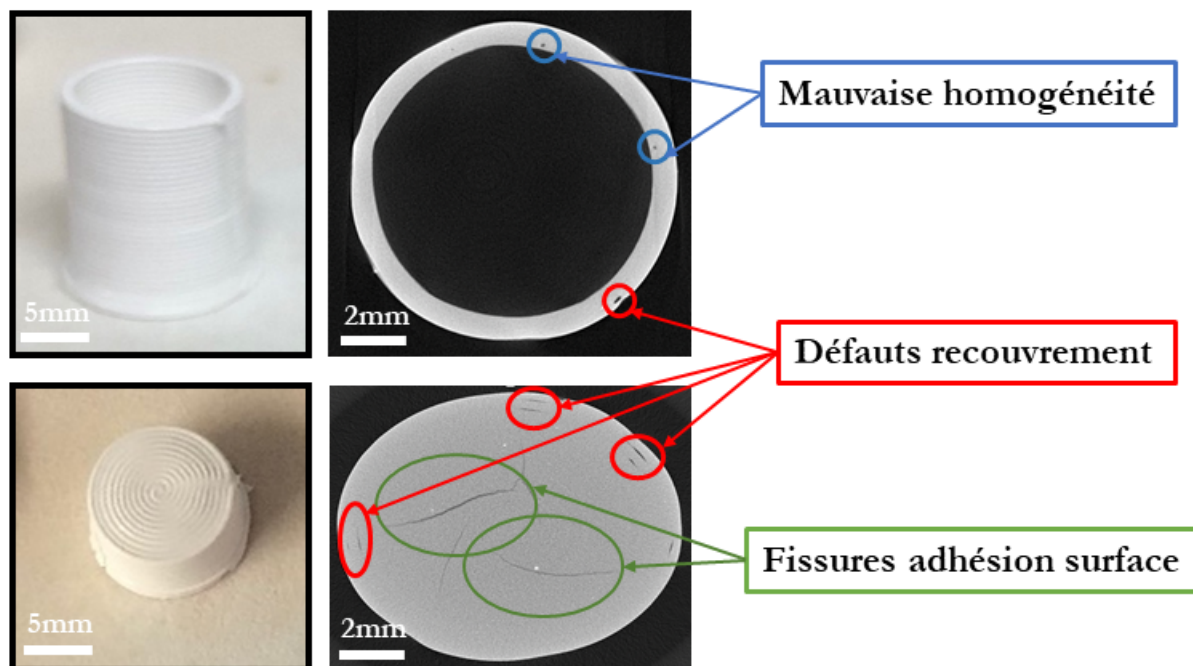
Photographies de deux pièces réalisées par robocasting et études des défauts par tomographie.
